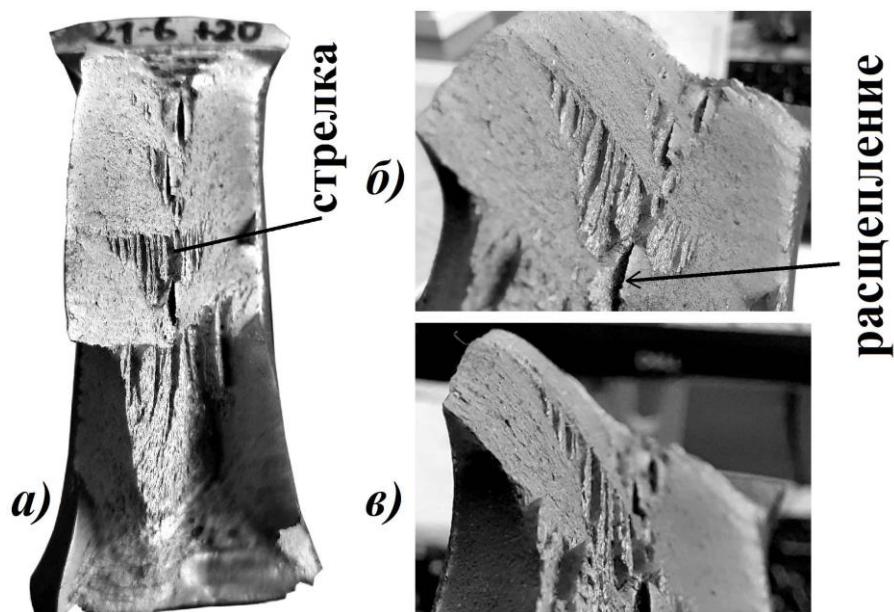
Внешний вид расположенной в средней по толщине части излома «размерной стрелки»: фронтальный вид (а); вид вдоль излома (б) и (в).
